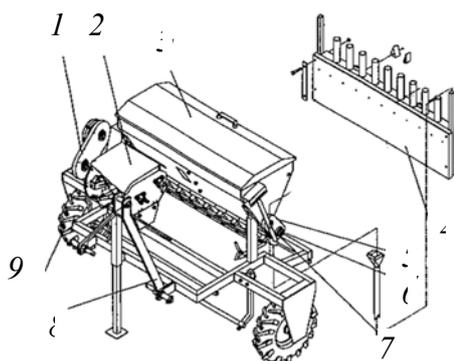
Общий вид сеялки «Egedal»: 1 – цепная передача; 2 – многоступенчатый редуктор с двадцатью передачами; 3 – бункер для семян; 4 – приставка для сплошного посева семян; 5 – цепная передача привода ворошилки семян; 6 – вал высевающих аппаратов; 7 – рычаг регулировки размера щели высевающего аппарата; 8 – рама с навеской; 9 – правое приводное колесо
